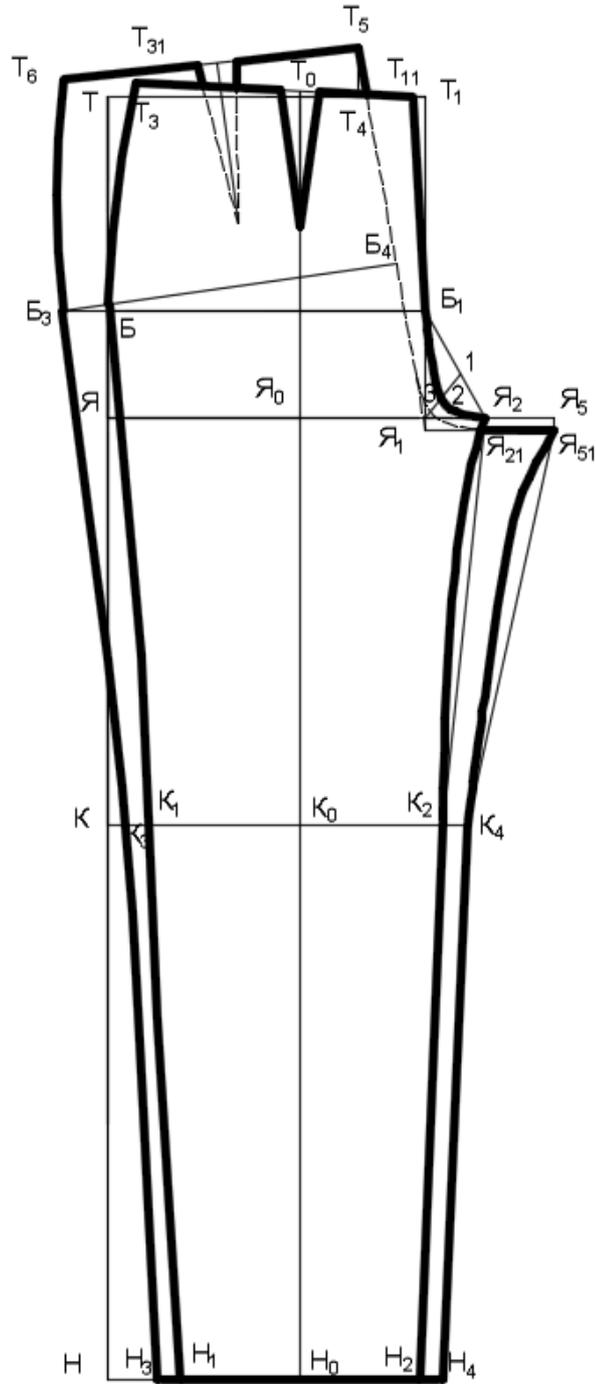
Схема построения чертежа конструкции женских брюк
